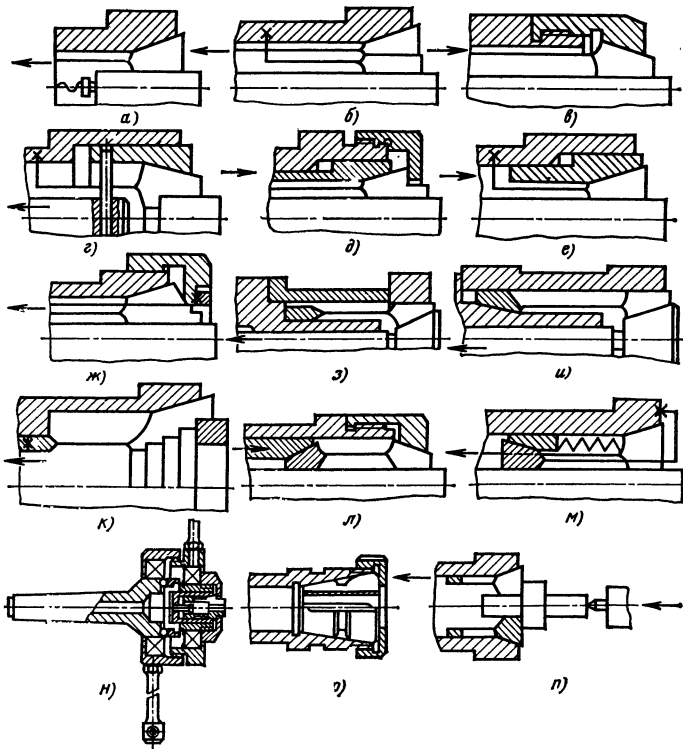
Конструктивные схемы цанговых приспособлений и патронов:
